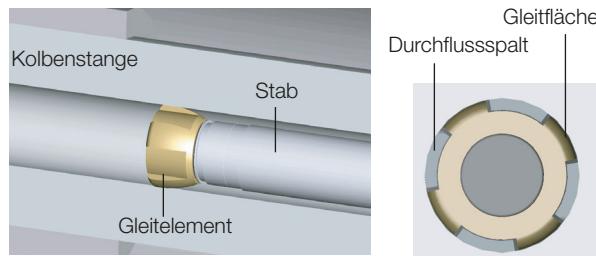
Detailansicht und Draufsicht Gleitelement
